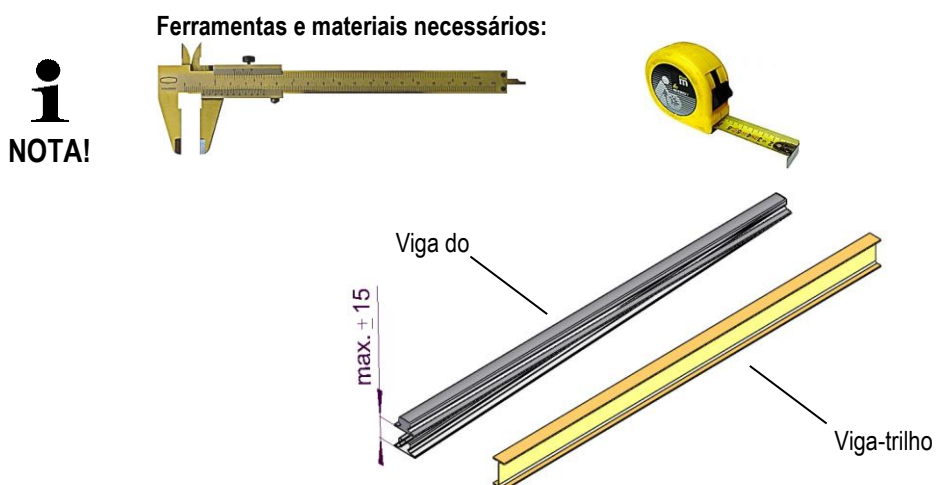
Alinhamento vertical ruim entre a viga do guindaste e a viga-trilho
